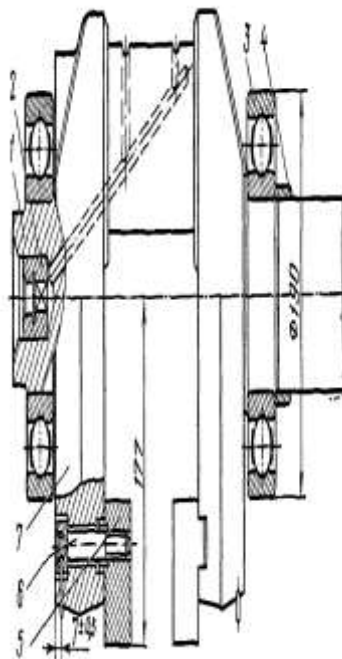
Колінчатий вал компресора КТ-6:
